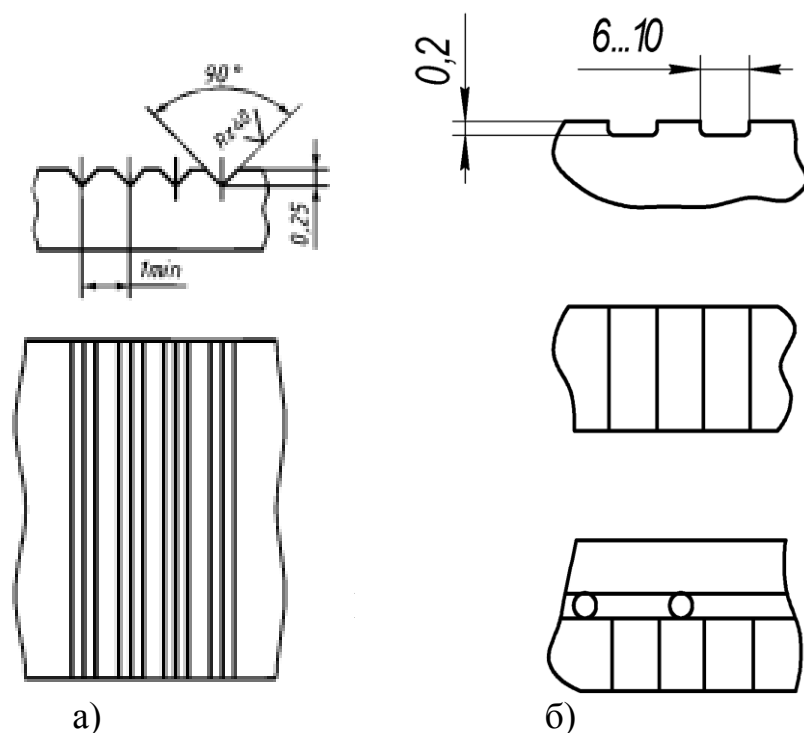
Вентиляционные каналы стержневых ящиков и вентиляционных плит
